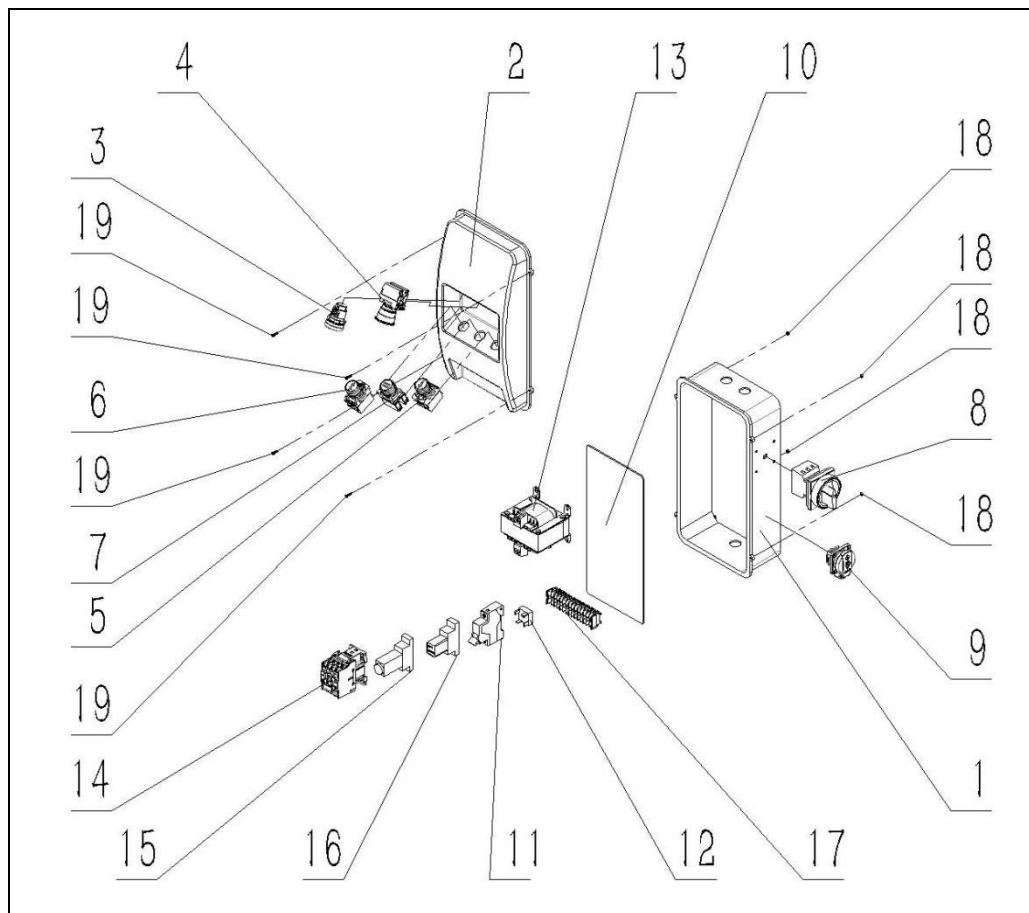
Explosionszeichnung des Steuerkastens des Hebebocks
